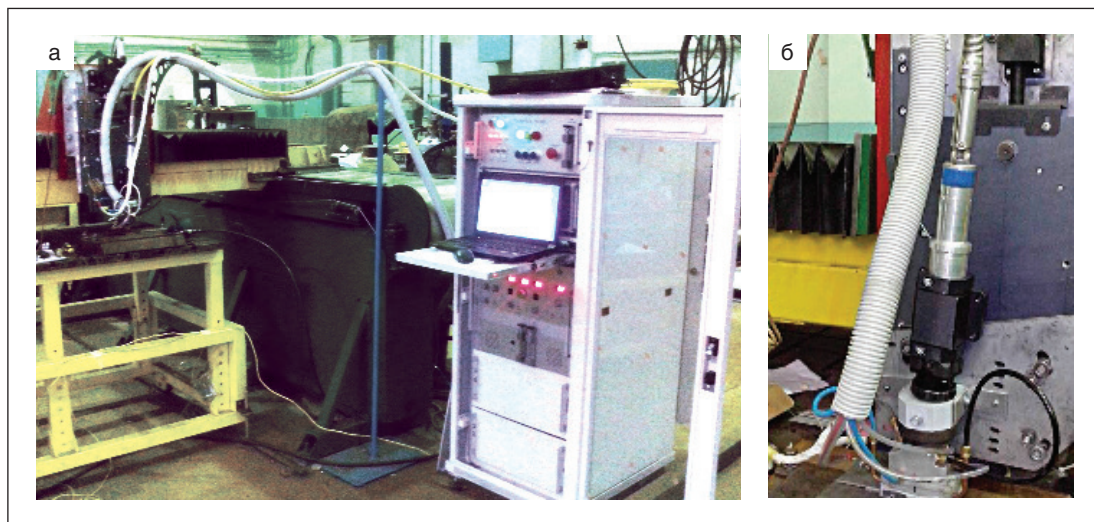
Внешний вид комплекса лазерно-микроплазменной сварки (а) и гибридного плазмотрона (б)
